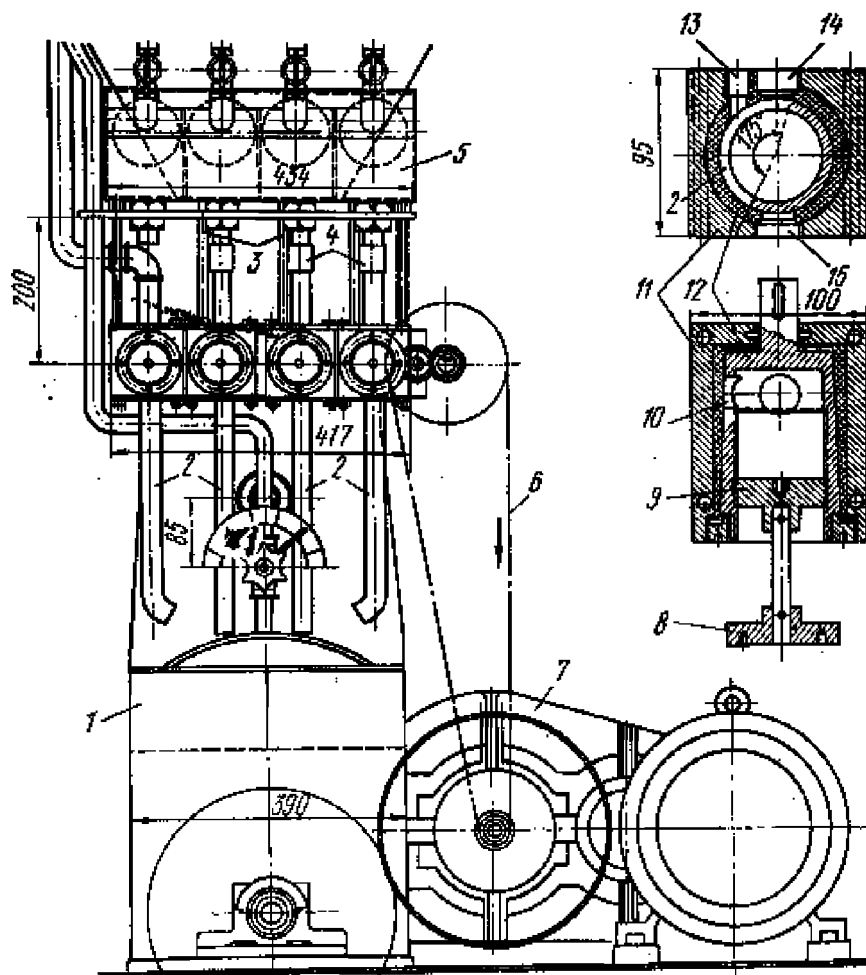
Стаканчиковий дозатор: 1 – ємкість; 2 – труба зливання відміряної порції; 3 – труба виходу повітря; 4 – труба для подавання рідини; 5 – бачок постійного рівня; 6 – ланцюгова передача; 7 – редуктор; 8 – штурвал; 9 – поршень регулювання об’єму; 10 – прямокутний проріз; 11 – корпус; 12 – мірний циліндричний стакан; 13 – канал для повітря; 14 – канал для рідини; 15 – отвір виходу рідини.
